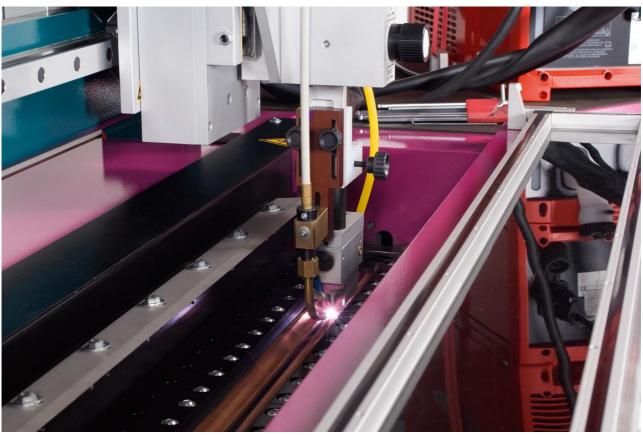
WIG Schweißverfahren mit Zusatzdraht (Option)
